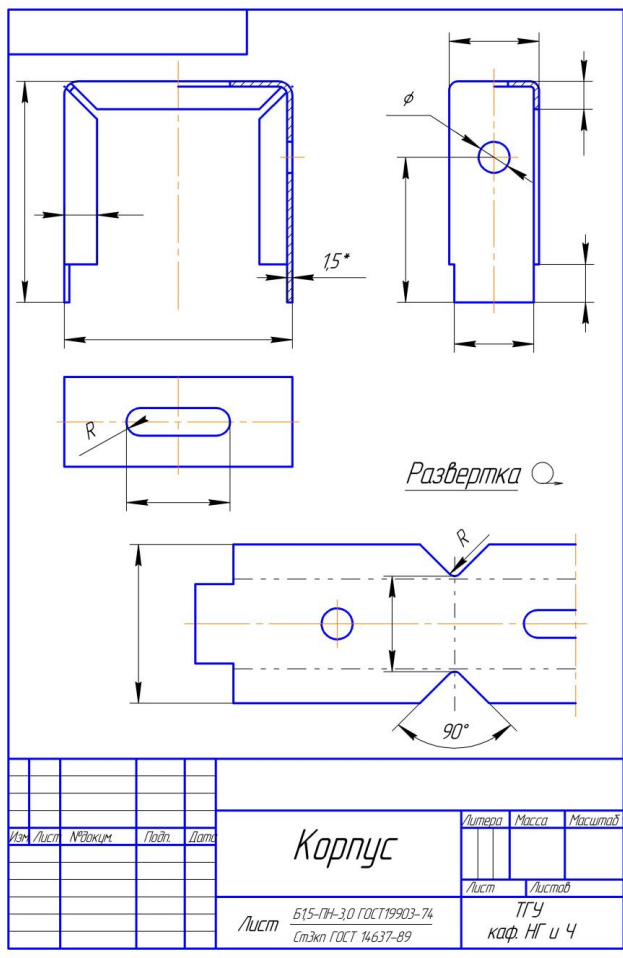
Чертеж корпусной детали, изготовленной штамповкой
